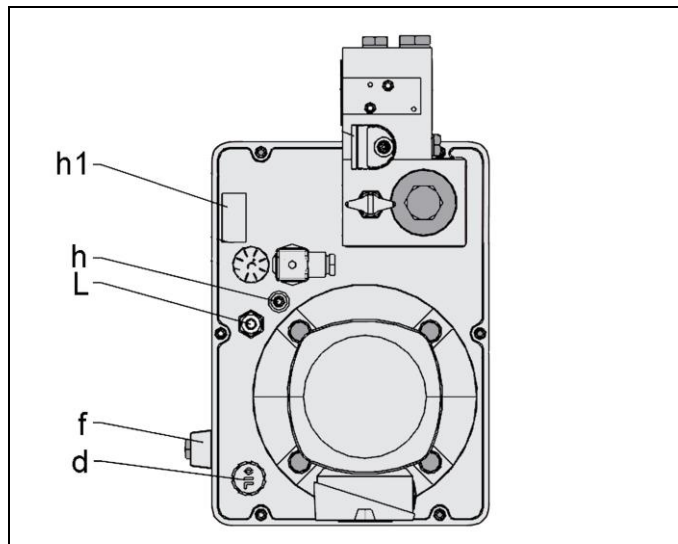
Illustration du couvercle du groupe hydraulique V11
